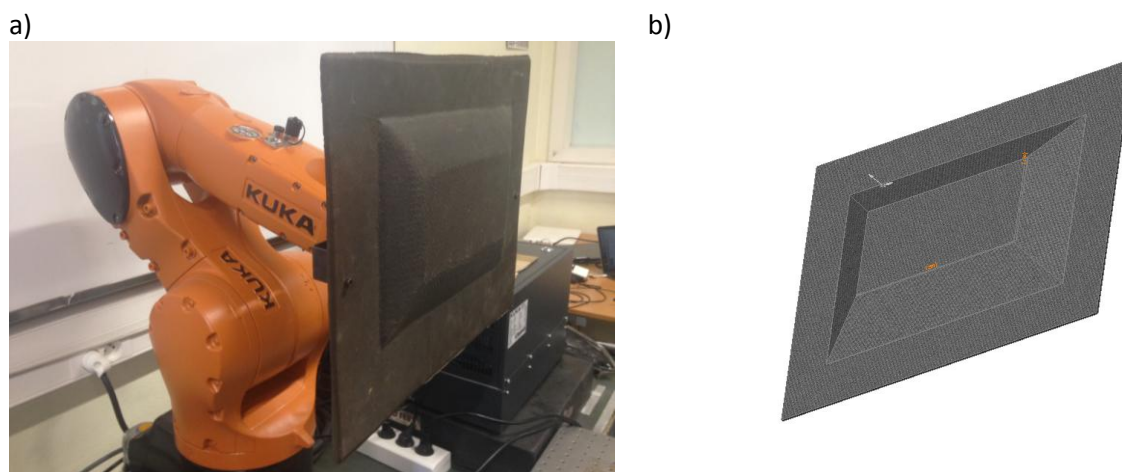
a), Pièce à analyser placée sur le robot 6 axes, b), Pièce dessinée en CAO.
